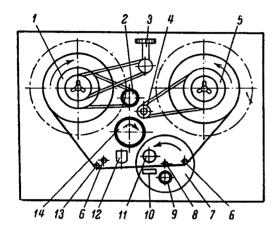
Кинематическая схема лентопротяжного мехаиизма.
